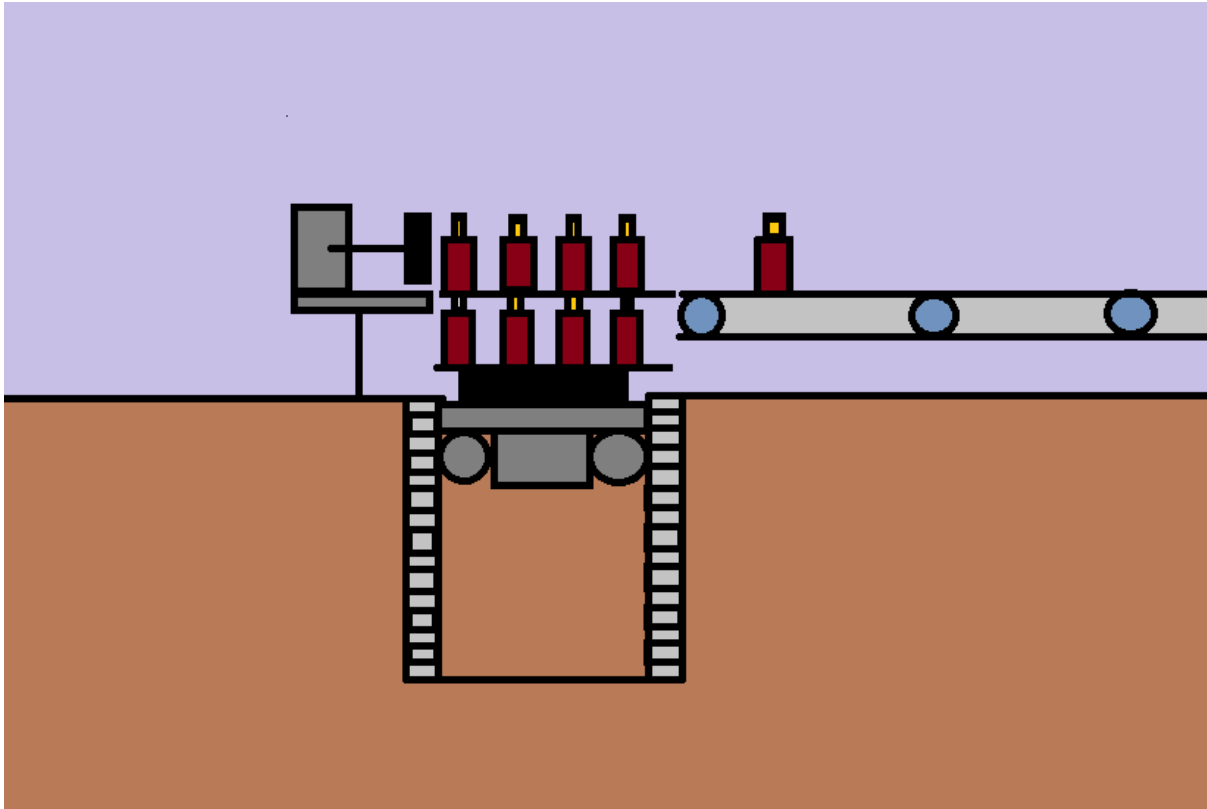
Propuesta de diseño de transportación mediante elevador y pistón vertical.
